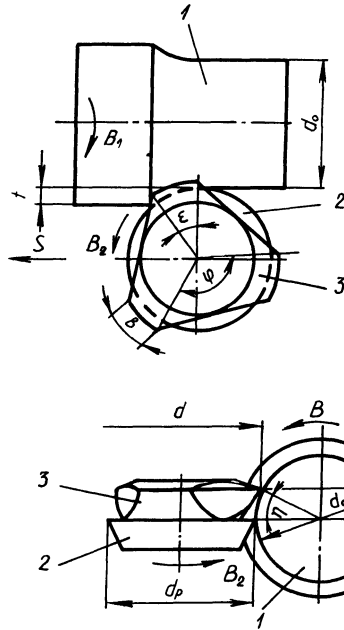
Схема обработки комбинированным инструментом с многорезвийным резцом
